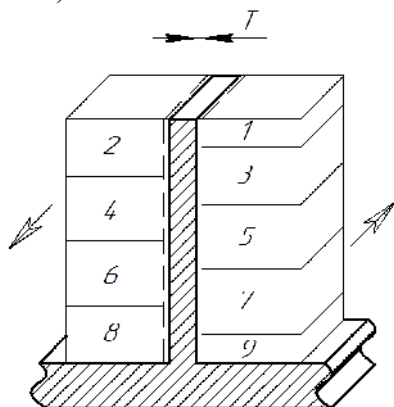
Траектория обработки тонкой стенки с перекрытием проходов
